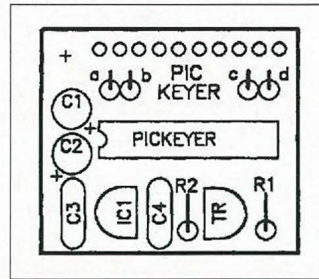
Placa de circuito impreso del PicKeyer, lado de componentes.
